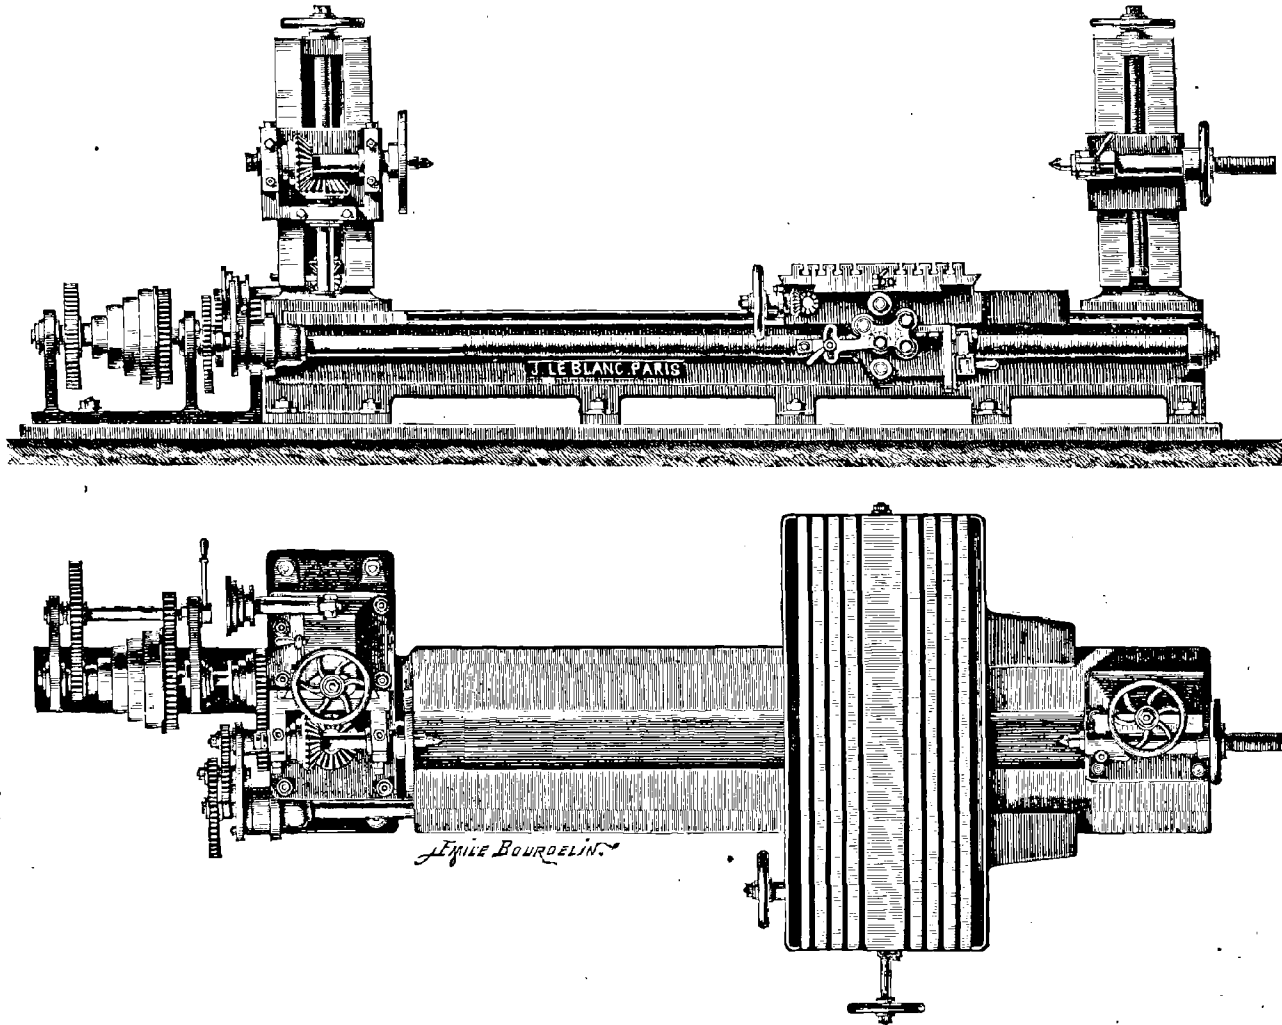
et 803. — Machine à aléser parallèle et à fraiser horizontale de J. Le Blanc.
